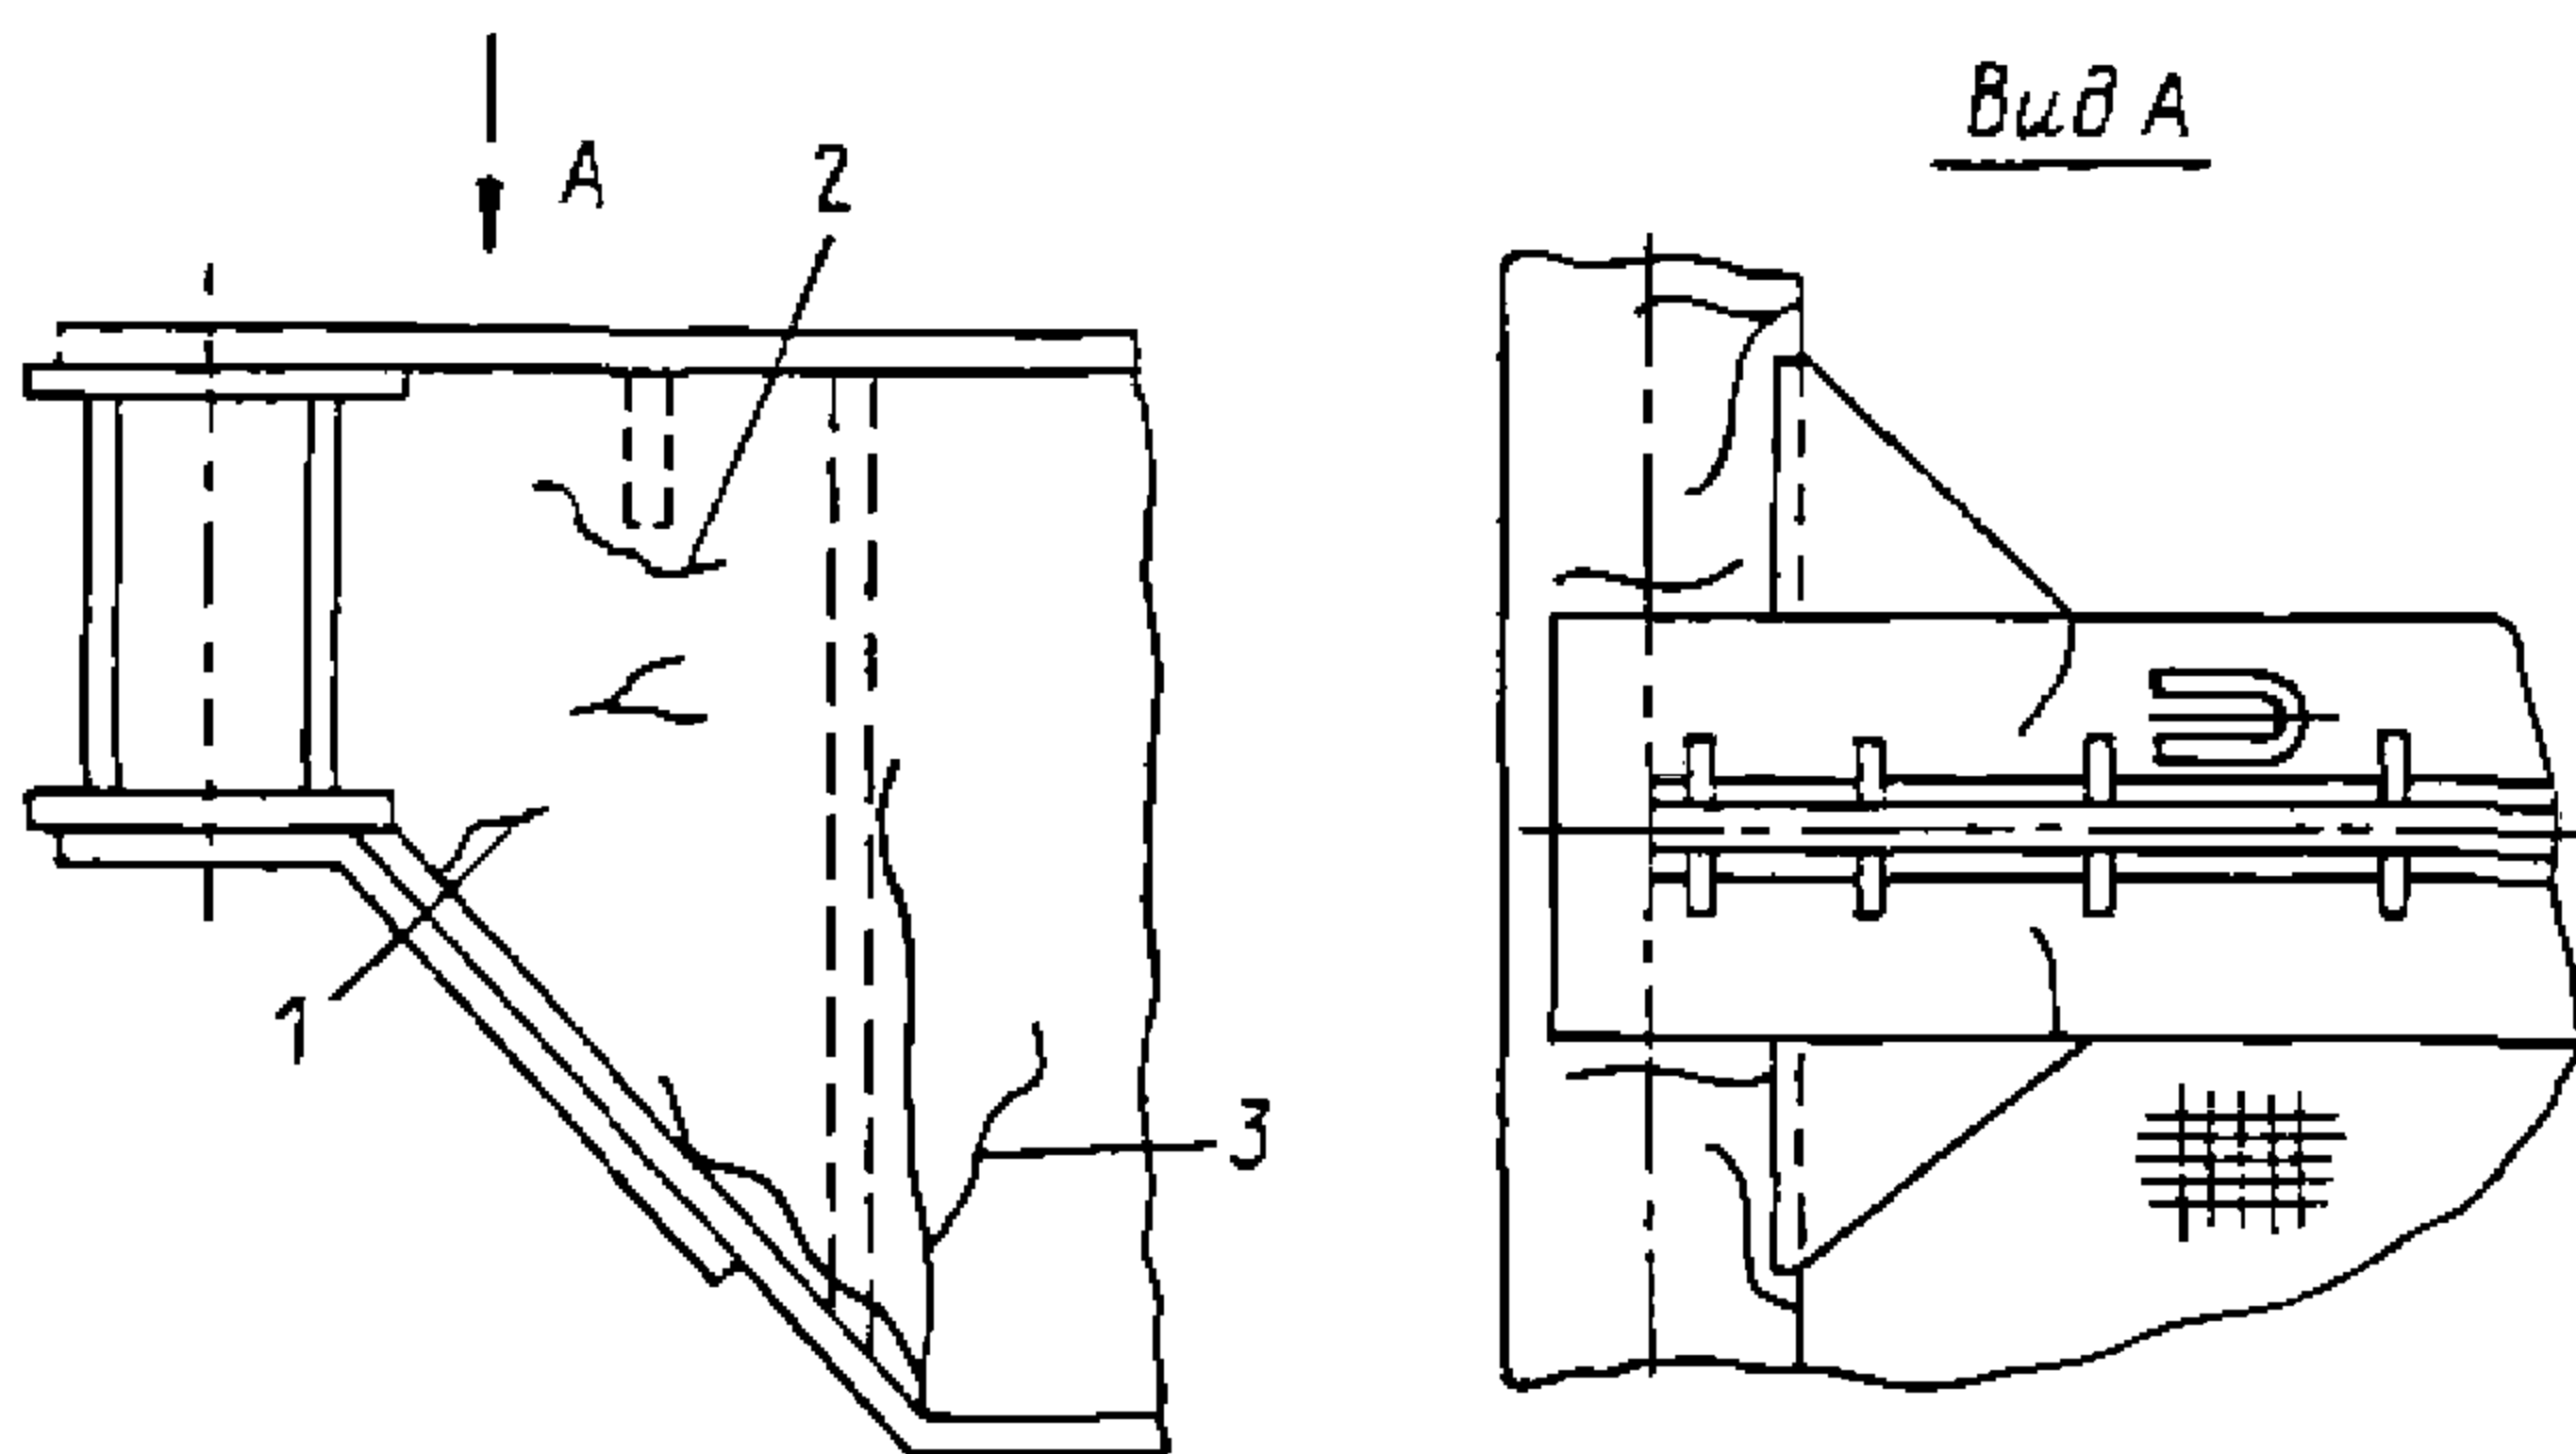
Трещины (1, 2, 3) верхнего пояса главных балок мостовых кранов
